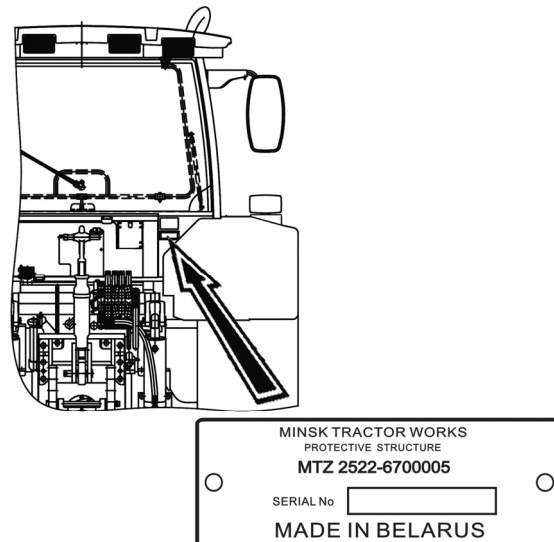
Место расположения маркировочной таблички кабины
